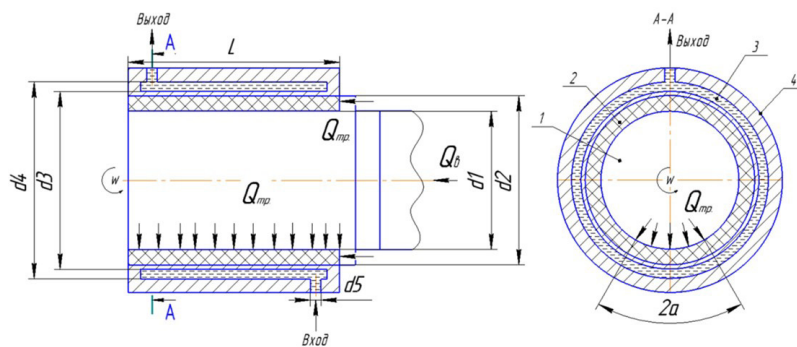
Принципиальная схема подшипниковых узлов турбоагрегата:
